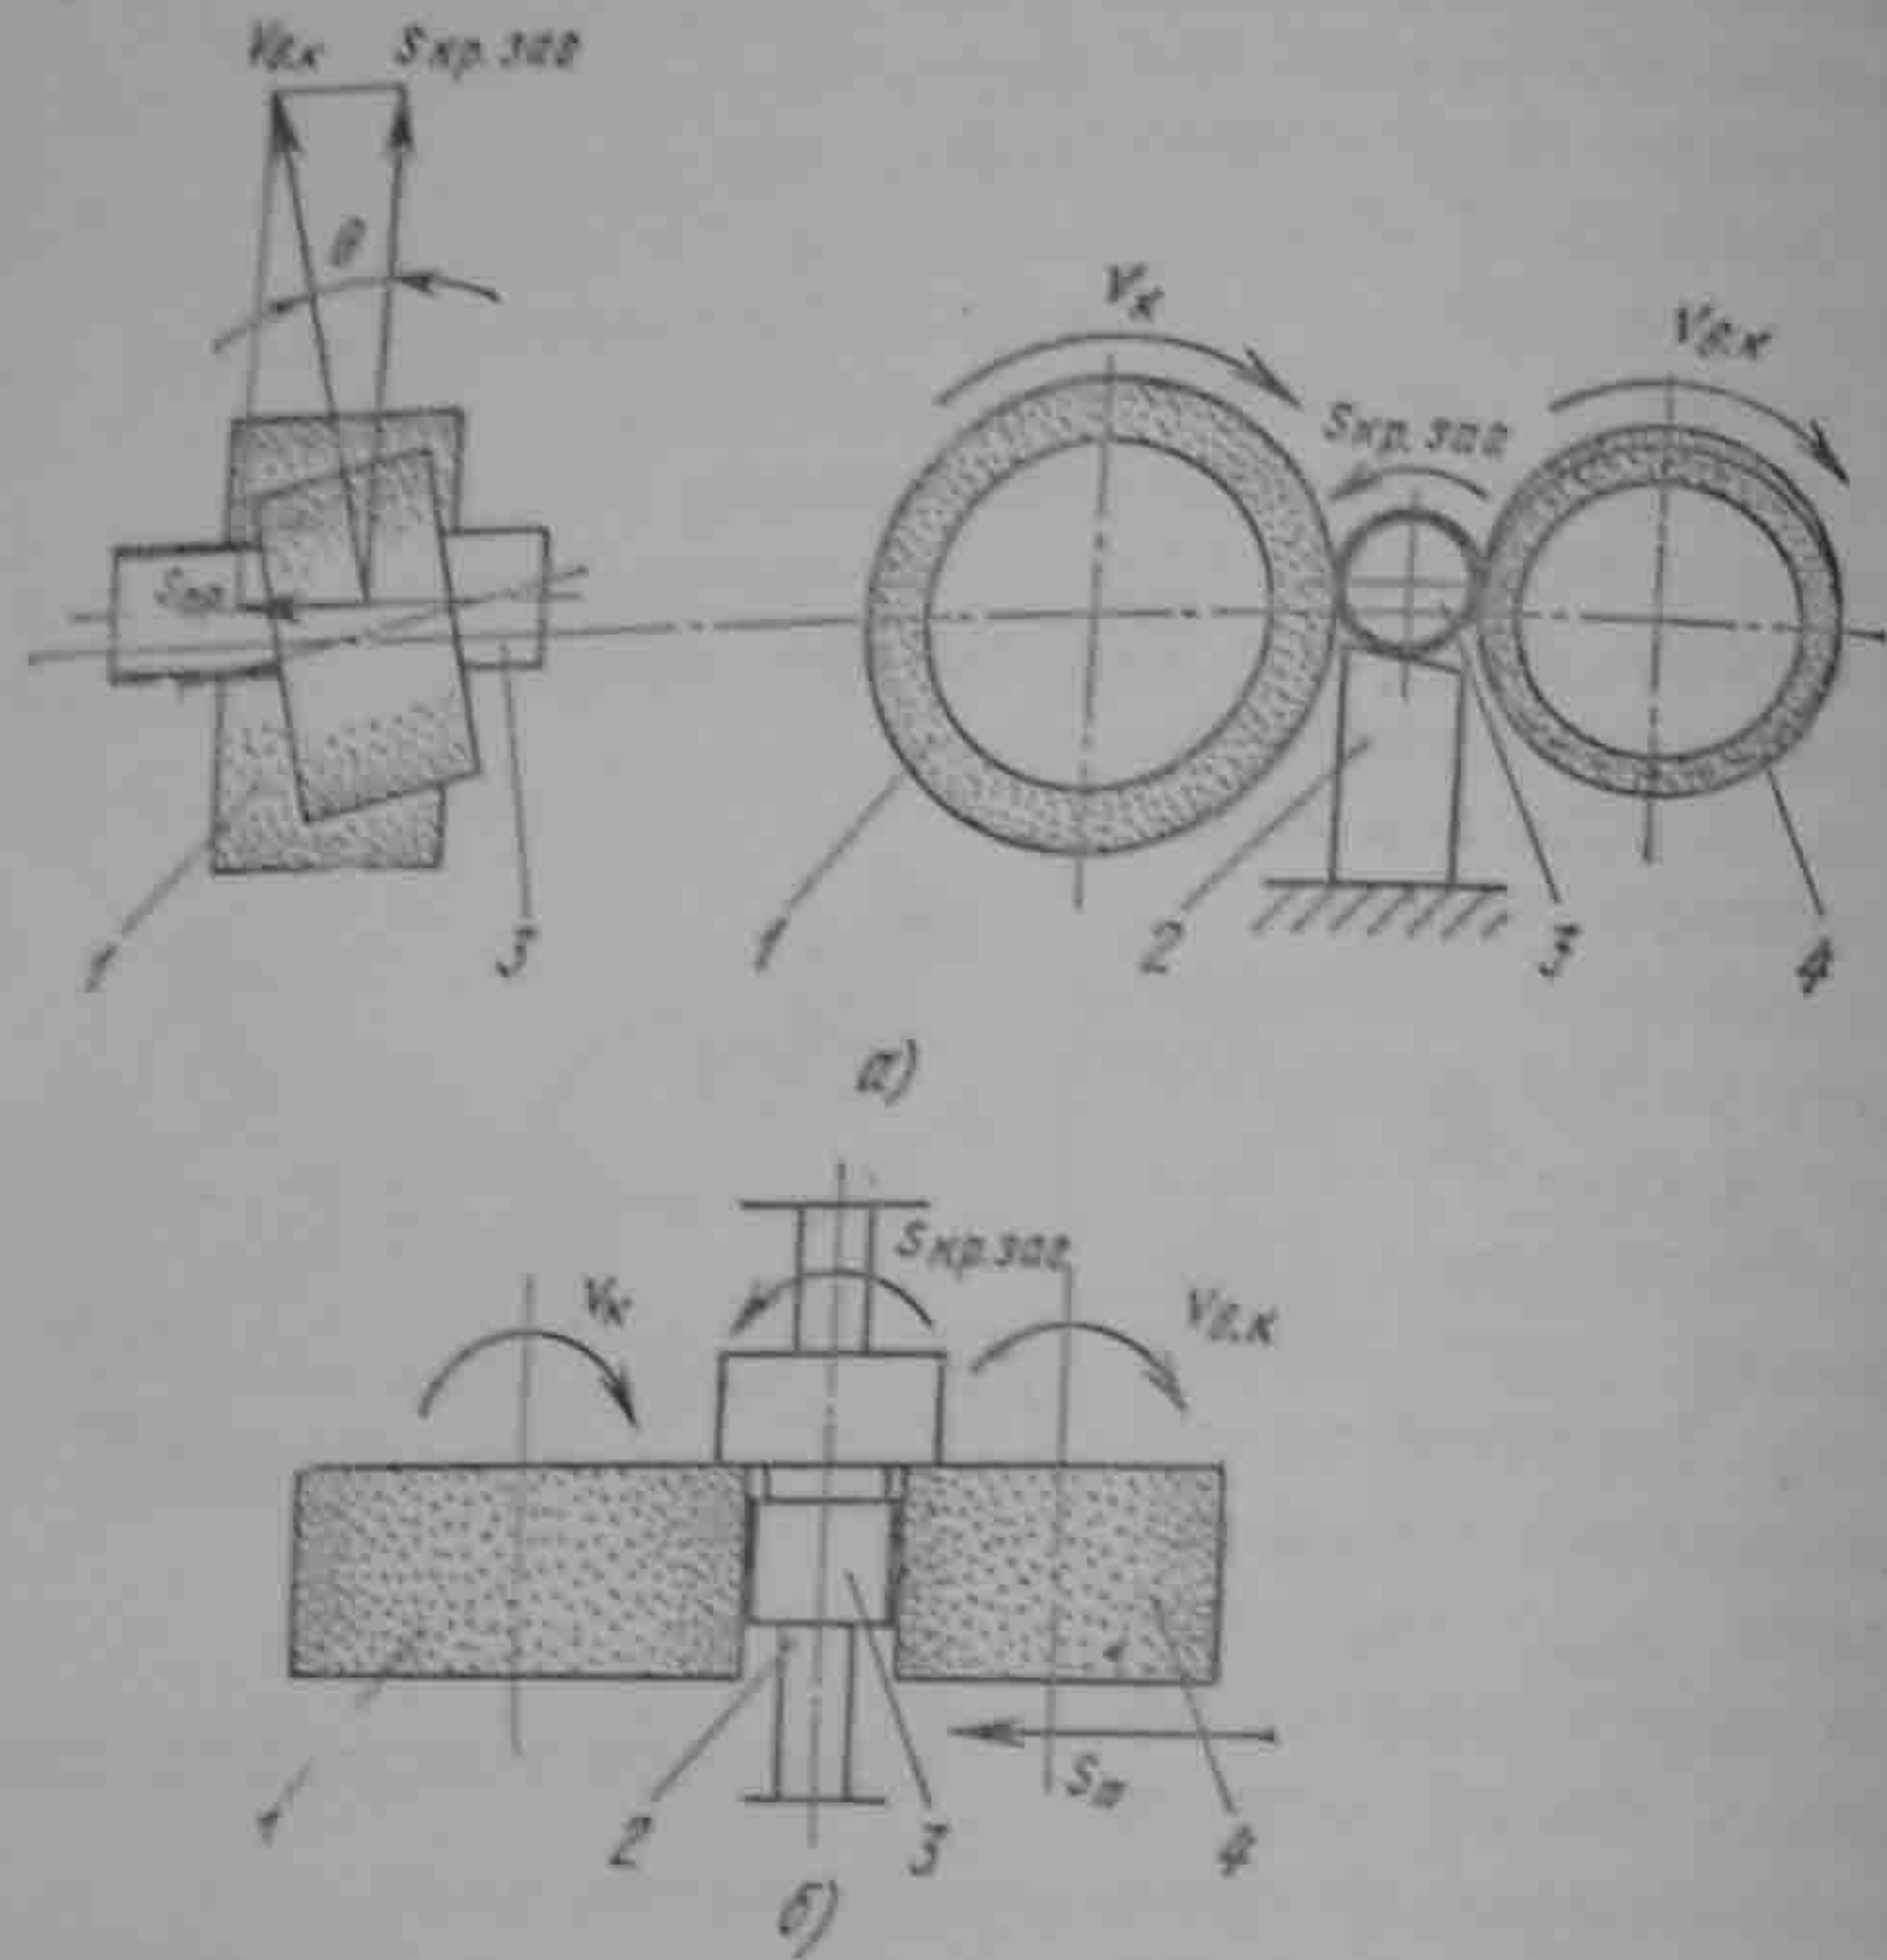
Схемы обработки заготовок на бесцентрово-шлифовальных станках
